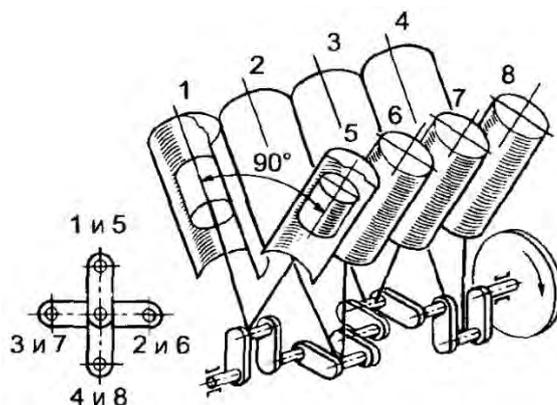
Коленчатый вал V-образного восьмицилиндрового двигателя
